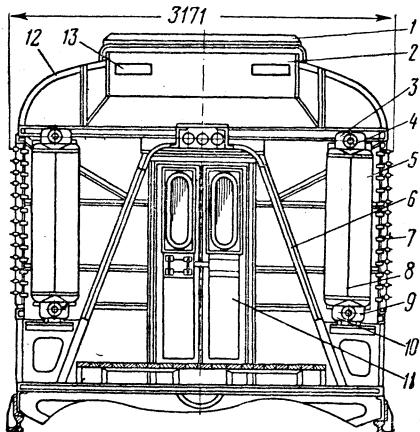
Поперечный разрез шахты холодильника дизеля на тепловозе ТЭ3:
